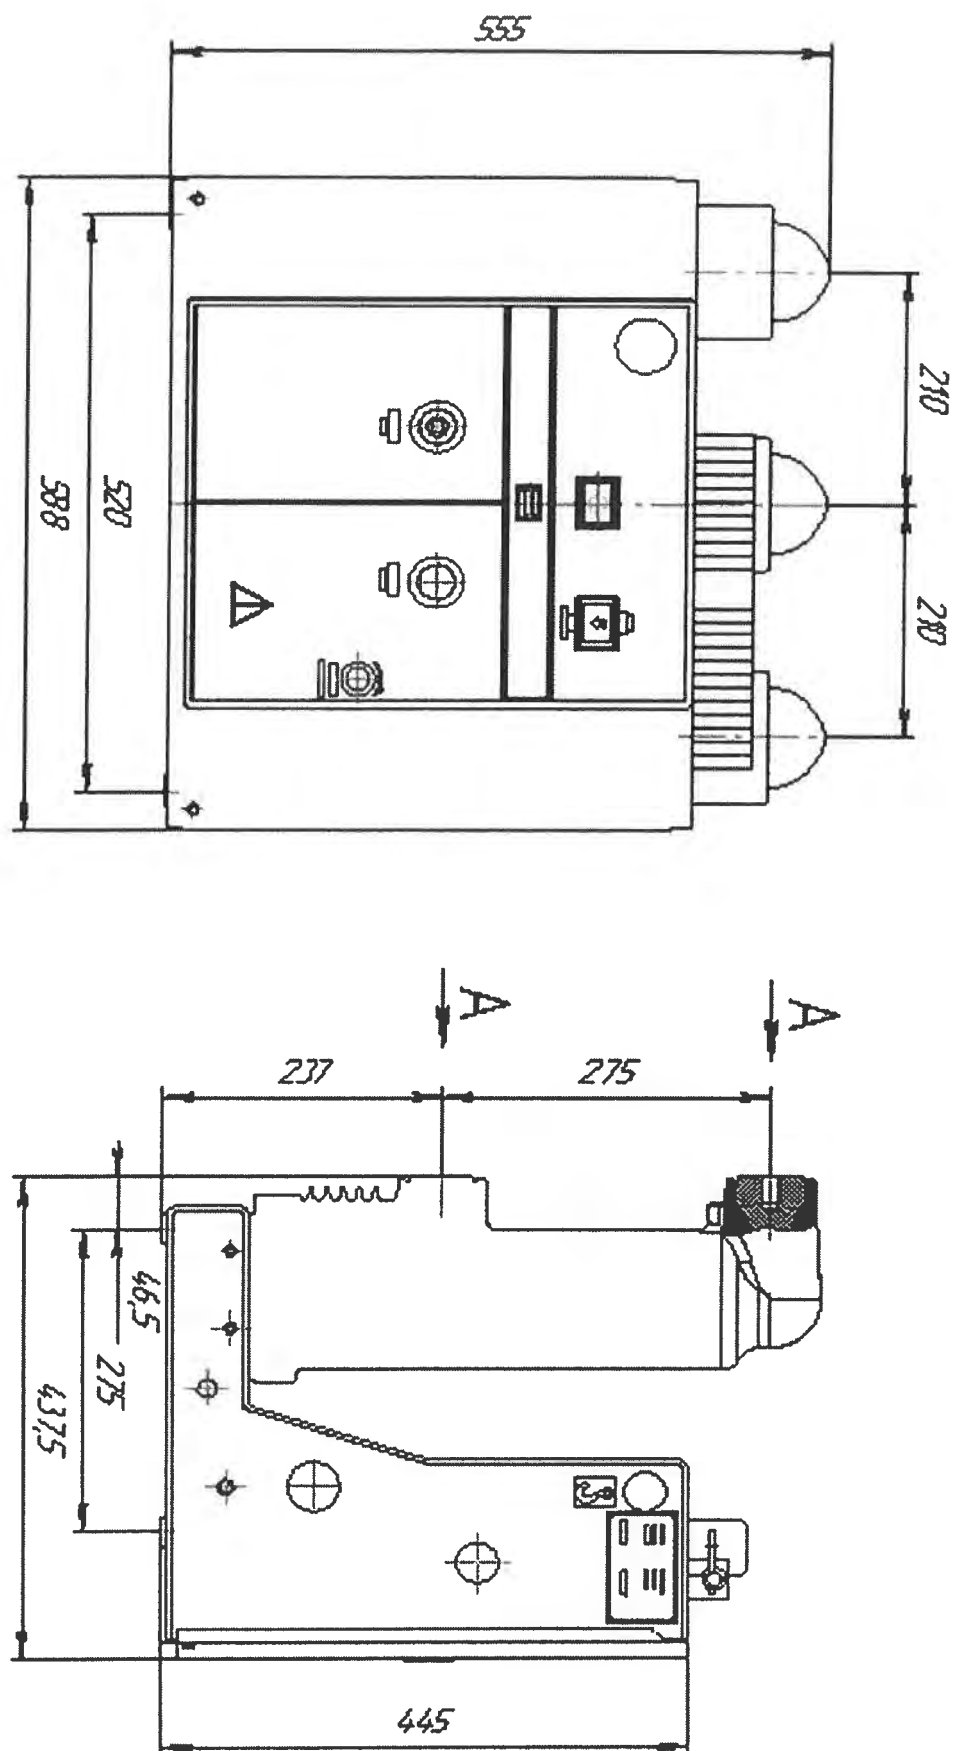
Габаритный чертеж выключателя вакуумного
